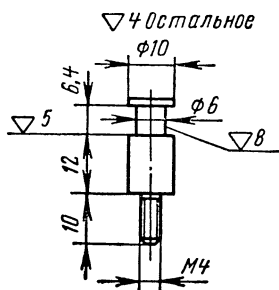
Направляющая колонка, латунь, хромировать, 2 шт.
